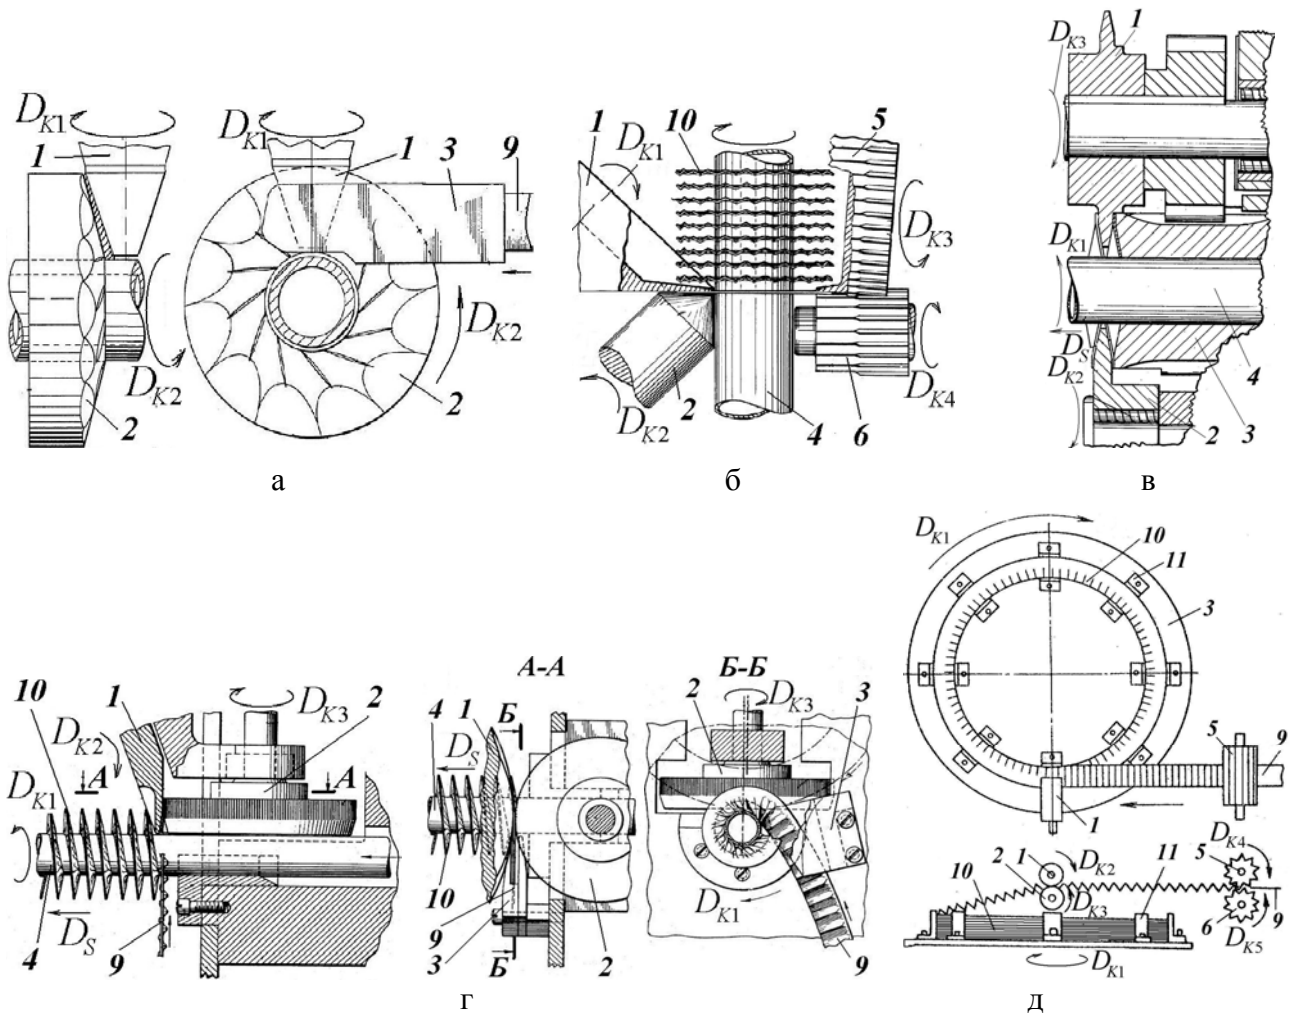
Схеми формоутворення ГГЗ шляхом навивання на ребро та одночасного асиметричного обтискування смуг між формувальними валками із профільними робочими поверхнями:
